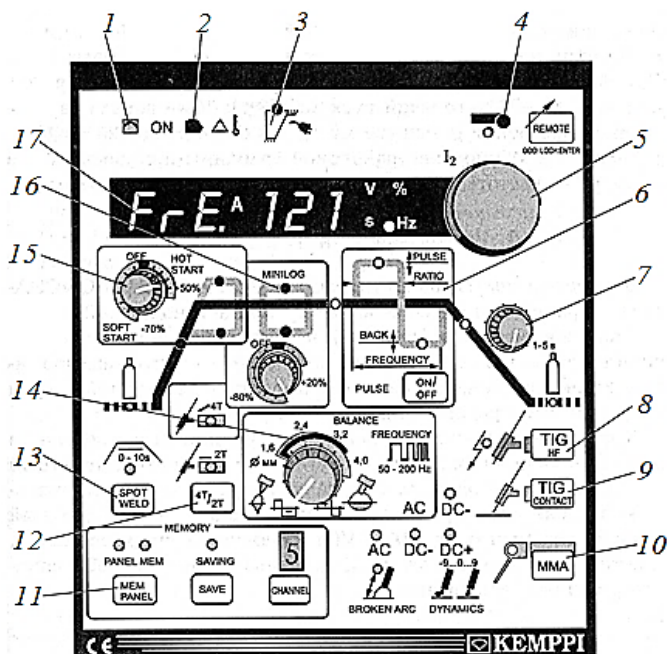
Панель управления установки для аргонодуговой сварки
